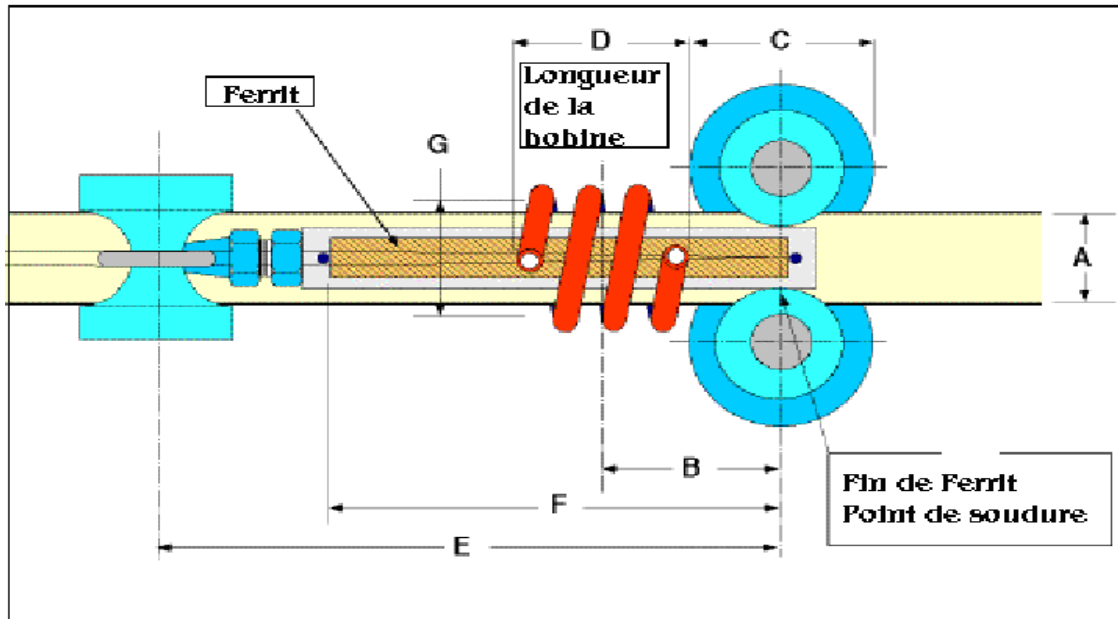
Cage soudeuse, dimensions et couplage Tube – inducteur
